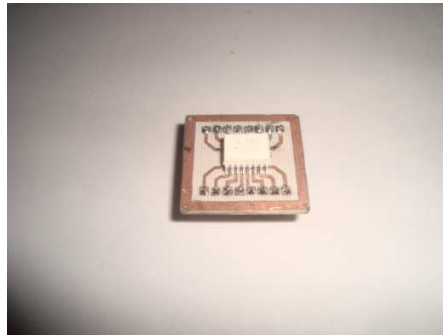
Drive HCPL-316J-000E montado en tablilla tipo DIP
